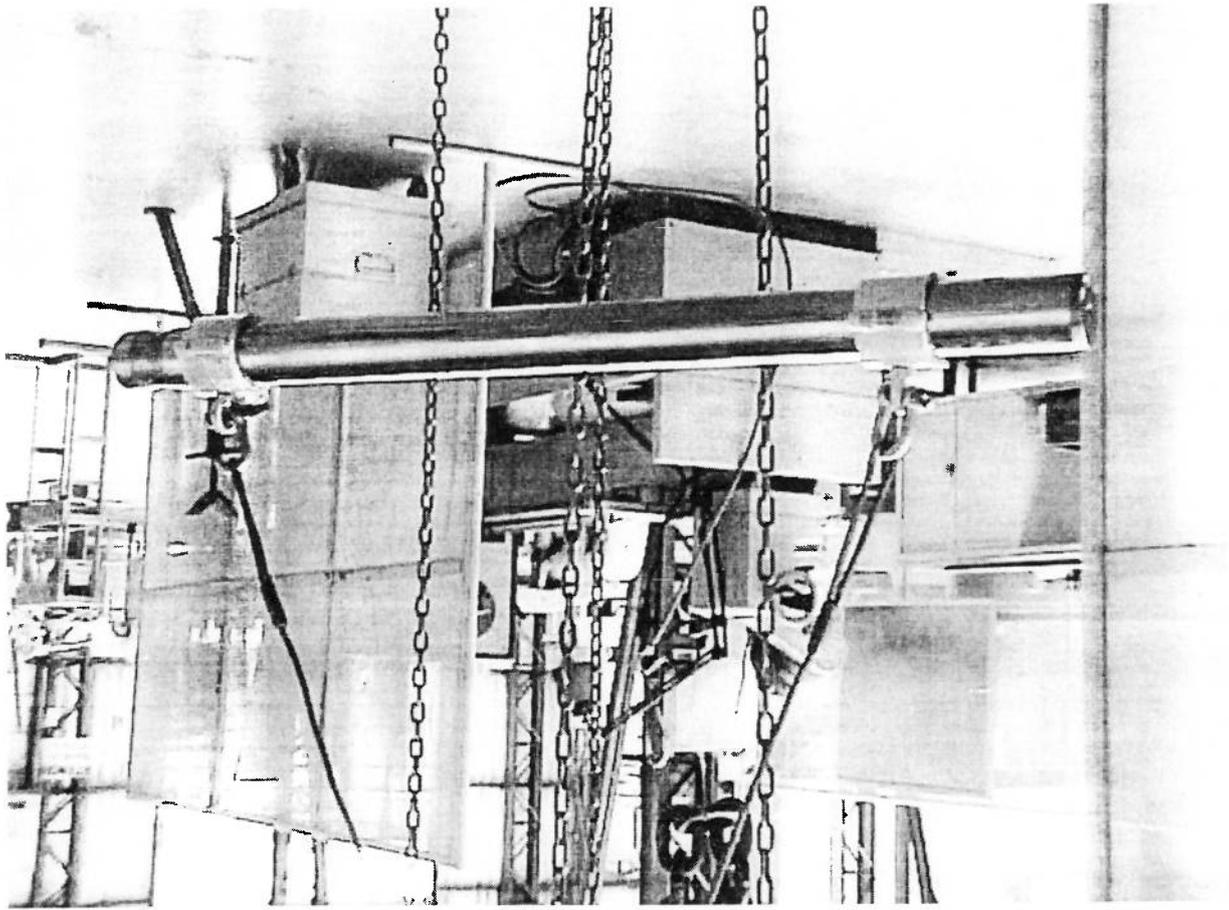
Vista do êmbolo sendo transportado para colocação em máquina entre pontas para execução do ensaio de ultrassom
